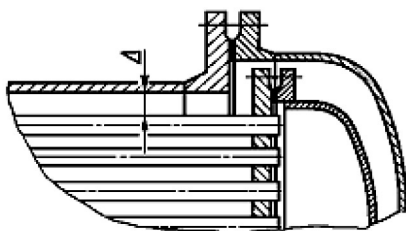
Вариант размещения крышки плавающей головки в кожухе меньшего диаметра
